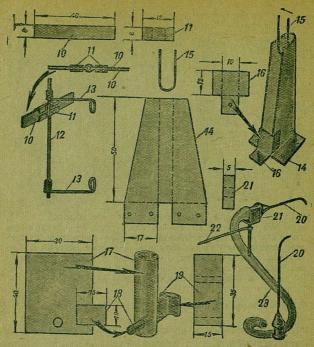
(продолжение). 10-пластинка якоря реле, 11-жестяные обоймы, скрепляющие пластинки якоря (припаяны), 12ось якоря, 13-проволочные подшипники оси якоря, 14развертка жести для стойки, 15-ограничитель, 16-скобка из жести, 17-жестяная заготовка для изготовления баллона пера, 18 - чернилоподающий цилиндрик, впаянный в отверстие баллона, 19 - жестяная скобка, скрепляющая баллон со стойкой лентопротяжного механизма, 20 - перо, 21 — хомутик пера, 22 — ограничитель проволоки. 23 — чернилоподающая резиновая трубка.
